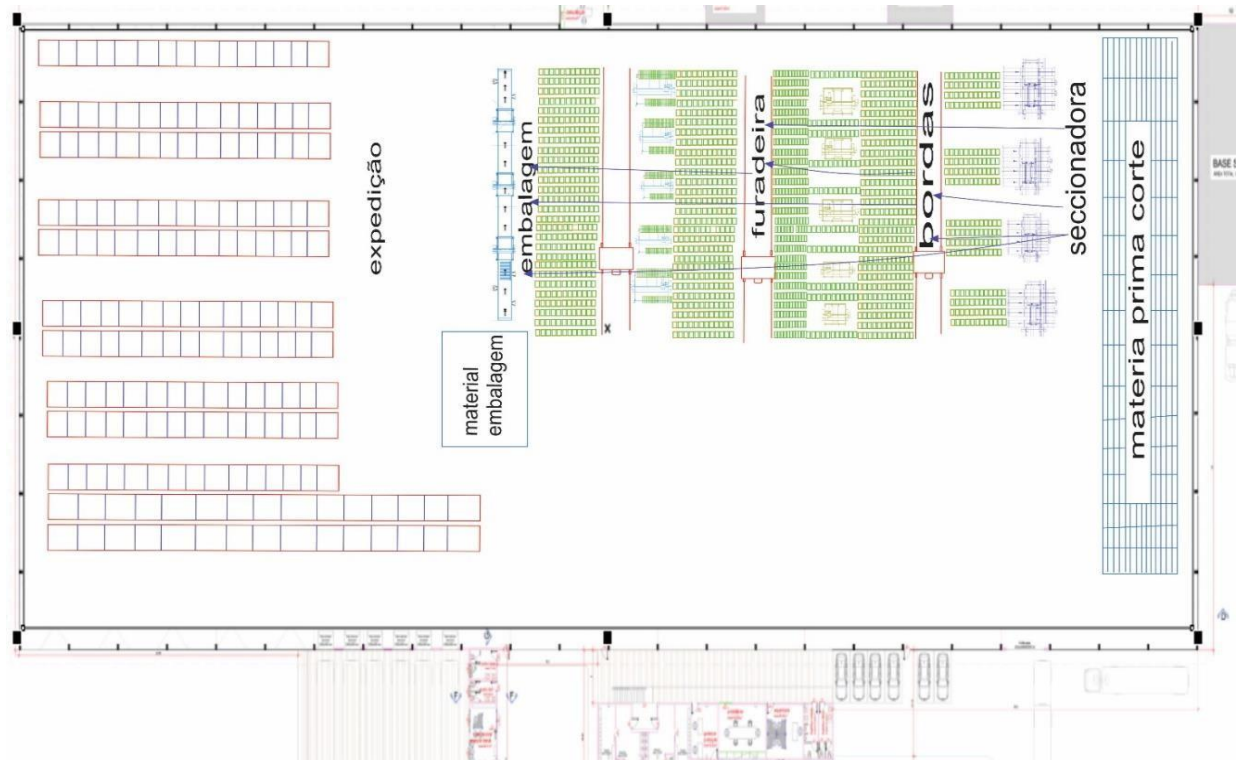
Planta Baixa Pavilhão Fellicci Moveis
